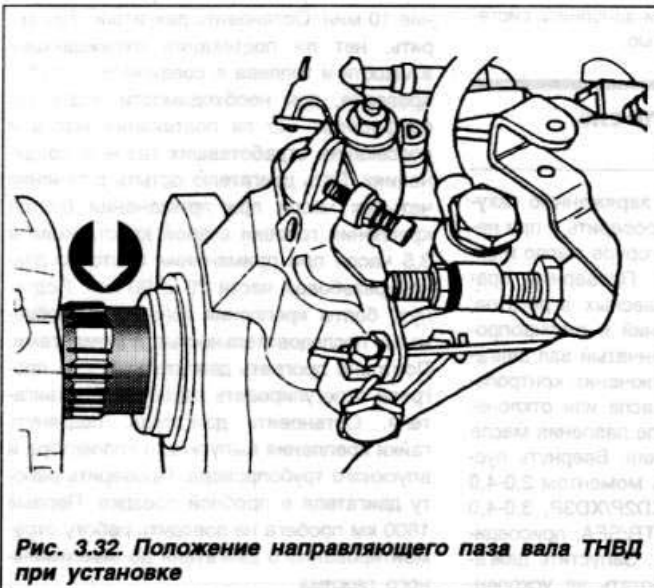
Положение направляющего паза вала ТНВД при установке
